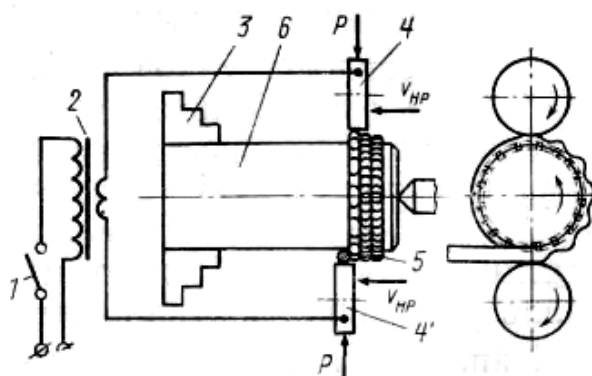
Двухточечная схема наплавки: 1 – прерыватель тока; 2 – трансформатор; 3 – кулачки патрона базового станка; 4 и 4' – наплавляющие ролики; 5 – наплавленный металл; 6 – металл основы
